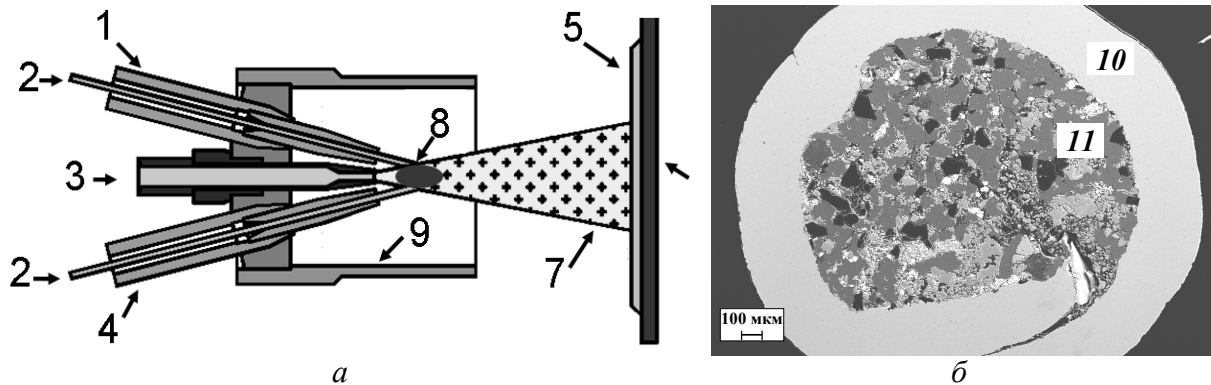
Типова схема металізатора для ЕДН покриттів (а) та поперечний переріз ПД (б): 1 – катод; 2 – ПД; 3 – стиснене повітря; 4 – анод; 5 – покриття; 6 – підложка; 7 – розплавлений метал; 8 – дуга; 9 – захисний кожух; 10 – оболонка; 11 – шихта.
